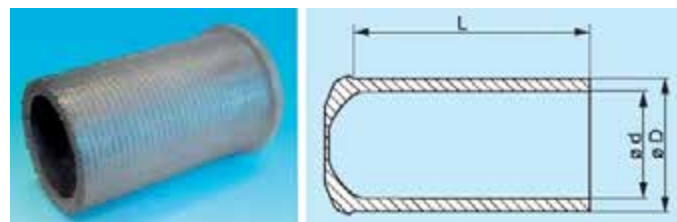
ro-45: Поставляемая фирмой *KS* заготовка втулки для сухой гильзы цилиндра; источник: MSI
